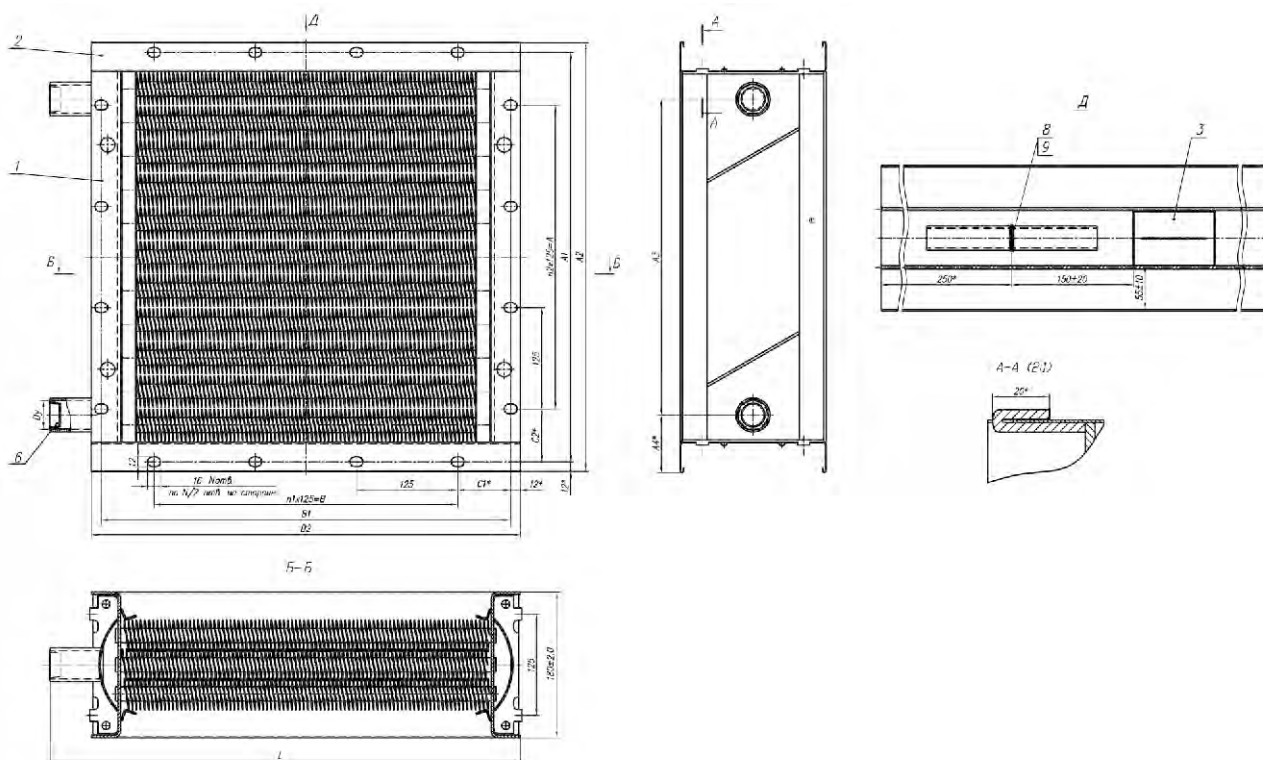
Габаритные и присоединительные размеры калориферов для А0.
